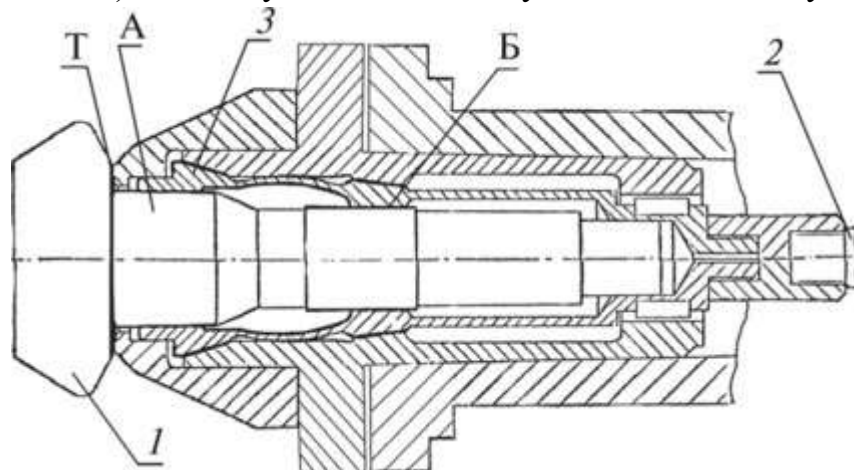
Схема цангового патрона для закріплення конічного валу-шестірні
